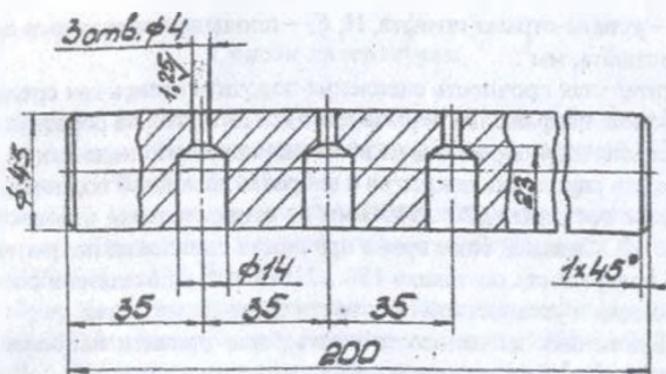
Образцы для определения прочности сцепления металлопокрытия с основным металлом.
